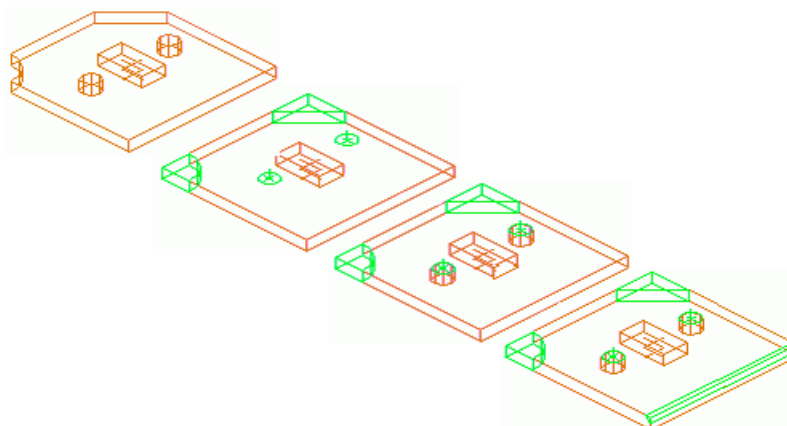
Типы представления пластины «стандарт», «обработки», «точно», «точно с обработкой для сварки»
